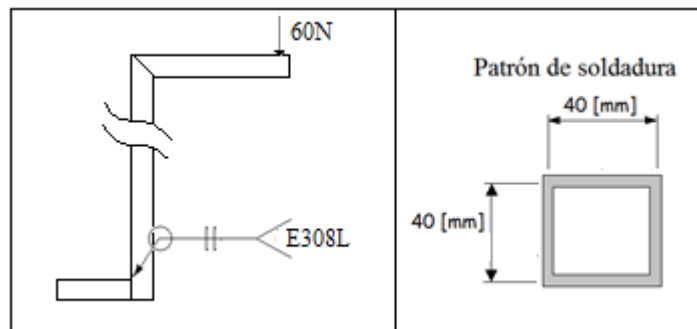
Diagrama de la soldadura en la junta superior
